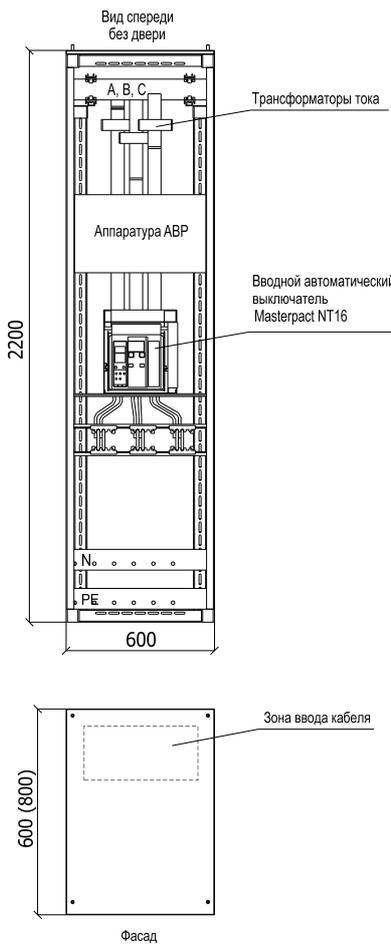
Чертеж общего вида НКУ ШУ-К-8600-В-1-(4974Х...5274Х)-ХХ УХЛ4
